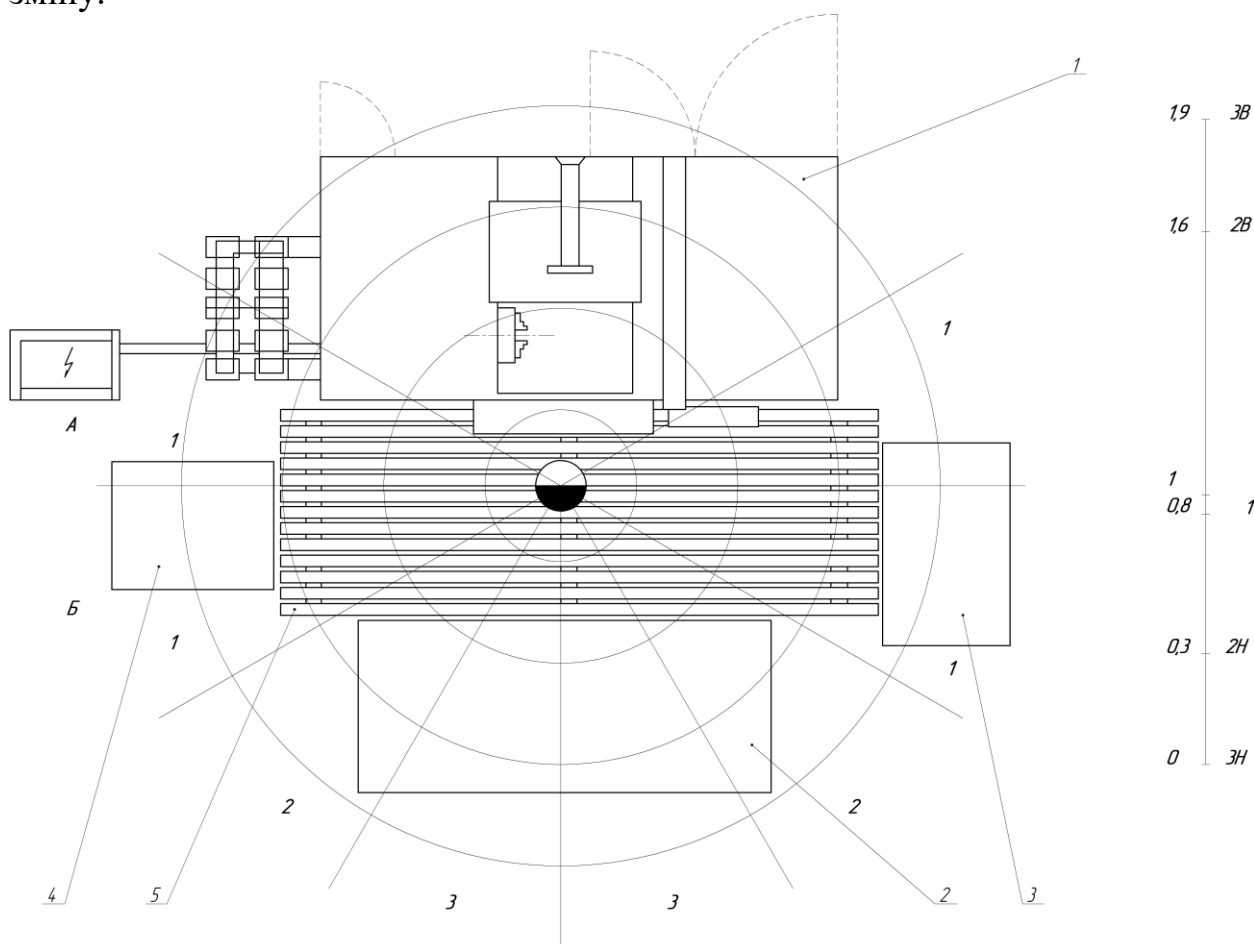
Планування робочого місця для токарного верстата САТ630 по виробництву деталей вал
